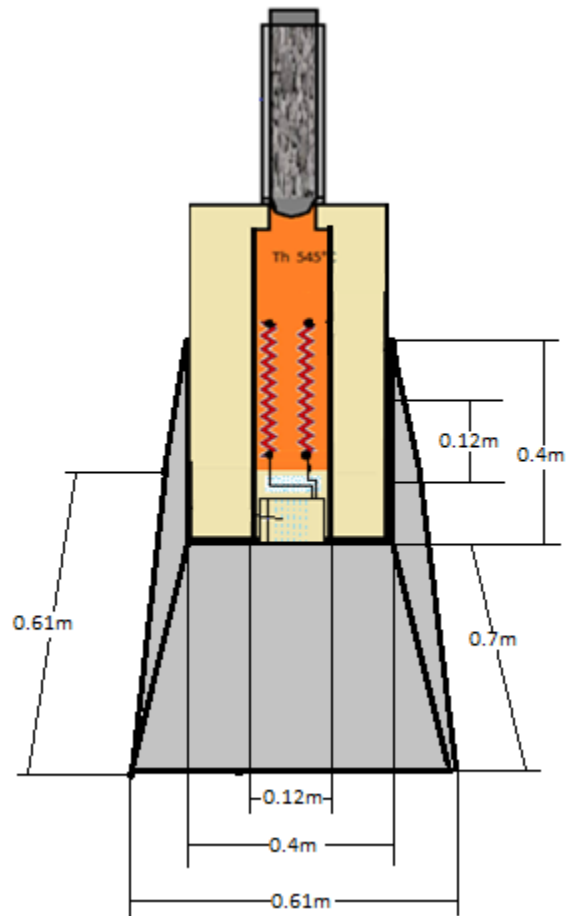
Estructura de soporte metálica. Fuente: Elaboración propia
